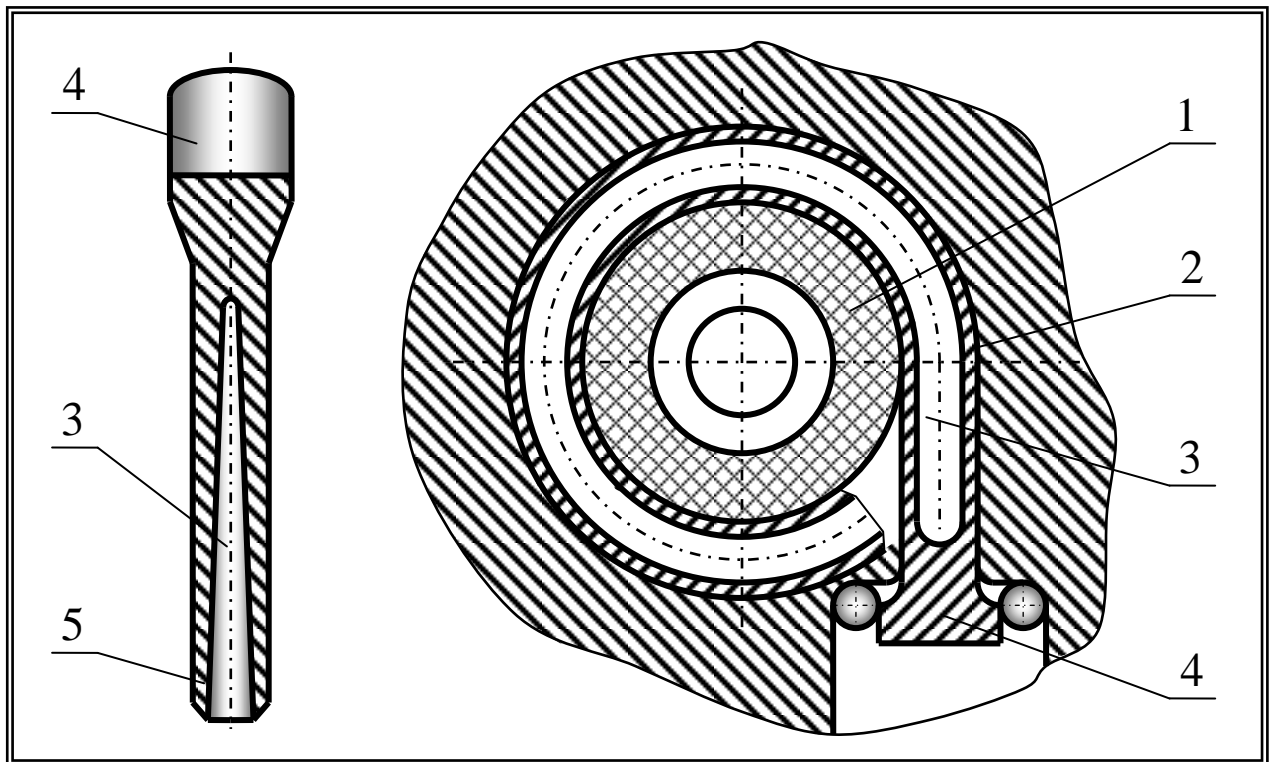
Схема крепления гидромониторного промывочного узла
